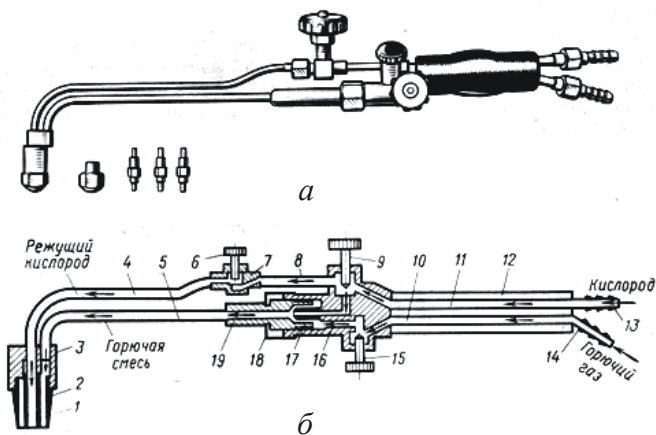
Универсальный резак «Маяк-1»: а – внешний вид; б – схема устройства резака; 1 – внутренний мундштук; 2 – наружный мундштук; 3 – головка; 4,8 – трубки режущего кислорода; 5 – трубка горючей смеси; 6 – вентиль режущего кислорода; 7 – корпус вентиля режущего кислорода; 9 – вентиль подогревающего кислорода; 10,11 – трубки кислорода и горючего газа; 12 – рукоятка; 13,14 – ниппели; 15 – вентиль горючего газа; 16 – корпус; 17 – инжектор; 18 – накидная гайка; 19 – смесительная камера
